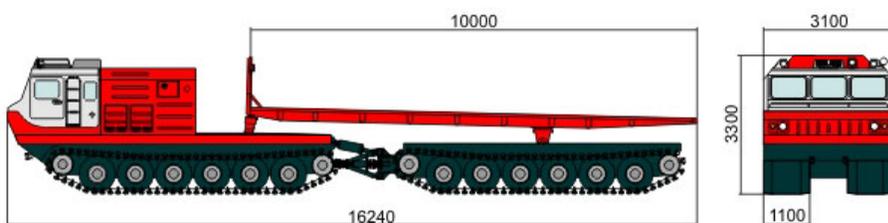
Сочленённый гусеничный транспортёр ДТ-30МН и его габаритные размеры¹¹.
